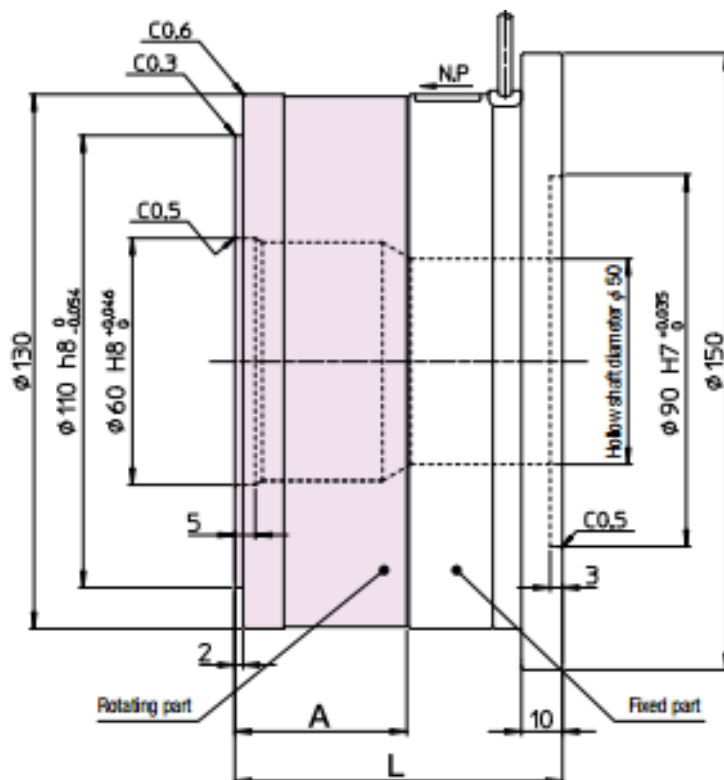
Габаритные и присоединительные размеры двигателя
